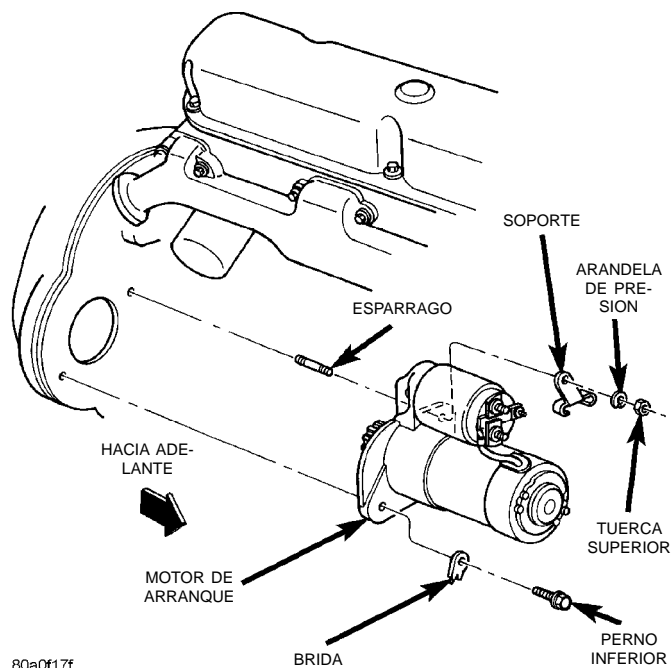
Desmontaje/Instalación del motor de arranque - Motor de 4.0L
